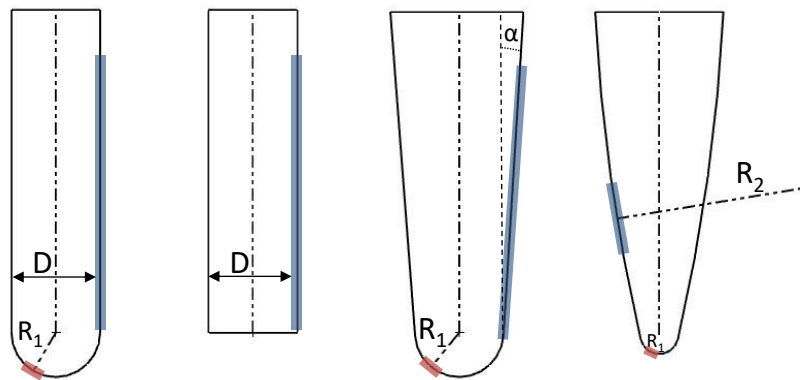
24 Contactos en la herramienta en operaciones de point y flank milling
